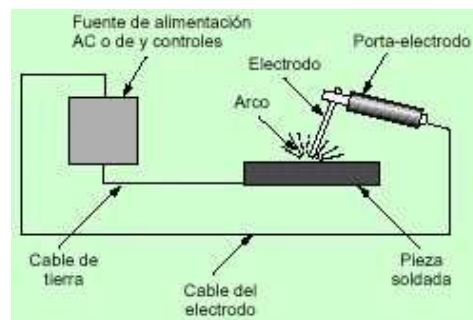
Esquema del proceso de soldadura eléctrica al arco
